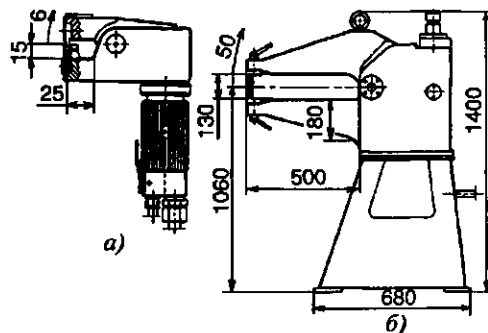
Инструмент для точечного скрепления листовых деталей: а – гидравлический ручной инструмент для деталей толщиной до 1,5 мм; б – стационарный пресс для деталей толщиной до 2,5 мм
